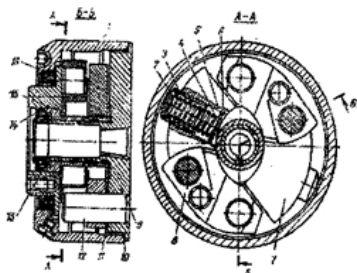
Муфта опережения впрыска топлива: 1 - корпус; 2 - регулировочные прокладки; 3 - стакан пружины; 4 -пружина; 5 - шайба; 6 - упорное кольцо; 7 - груз с пальцем; 8 -проставка с осью; 9 - ведомая полумуфта; 10 -уплотнительное кольцо; 11 - шайба; 12 - ось грузов; 13 - ведущая полумуфта; 14, 16 -сальники;15 - втулка ведущей полумуфты.
